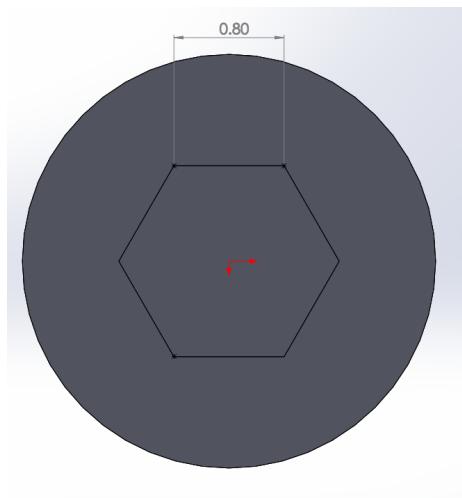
Etapa 2 da fabricação do pino de acoplamento do motor à válvula - Vista inferior
